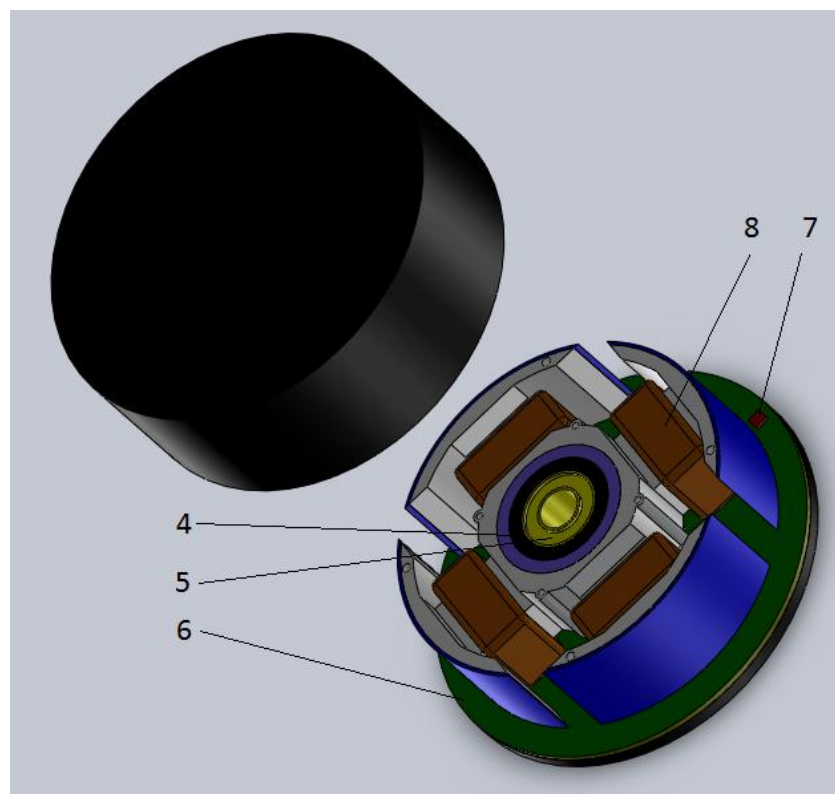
Řez motorkem s radiálním tokem – vnější rotor
